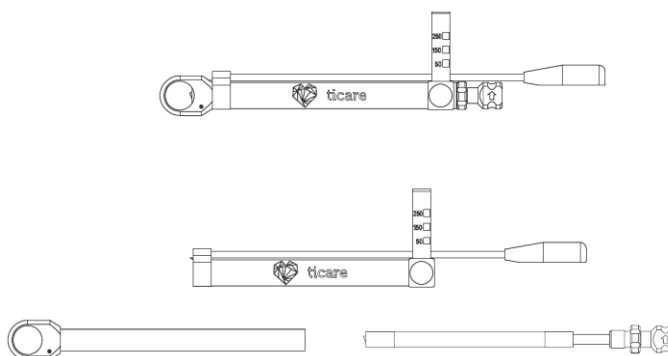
Despiece de la llave de carraca desmontable dinamométrica 250 Ncm
